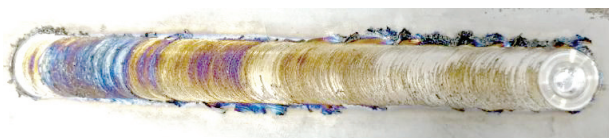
Образец, полученный с использованием приспособления, представленного на рис. 3
